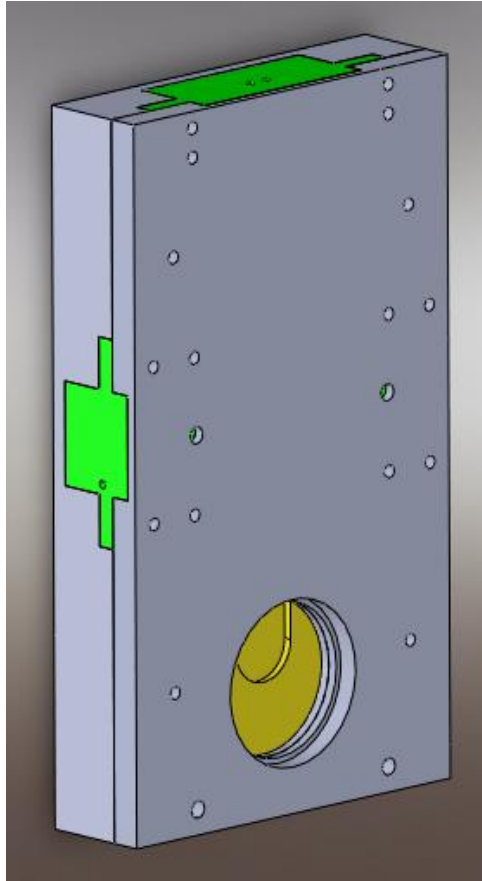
Conjunto del molde de metacrilato en posición real (vertical).
